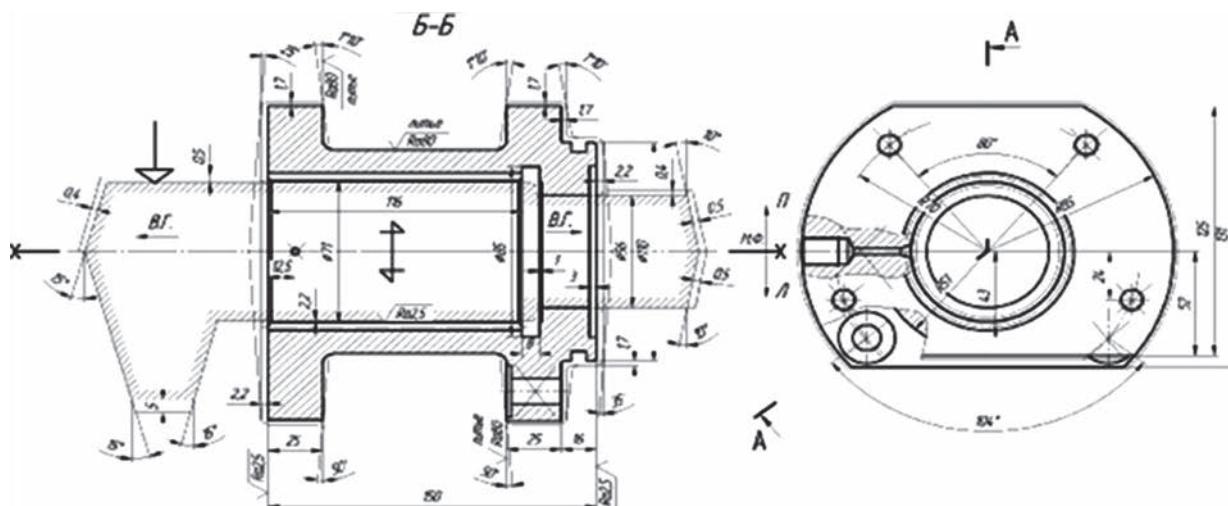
Чертеж детали «Корпус» с литейно-модельными указаниями
